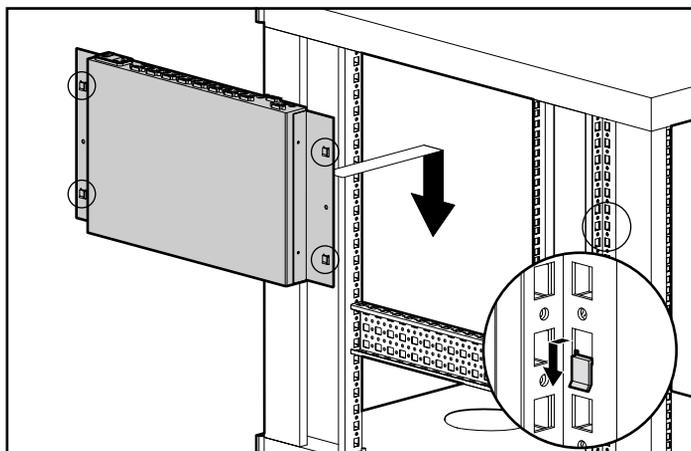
Montaggio dell'unità sulla parete laterale del rack
